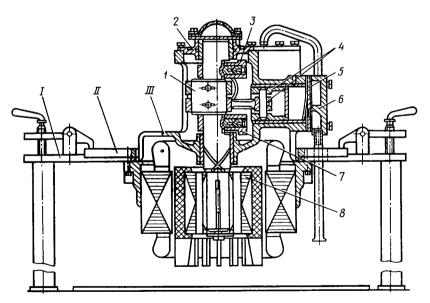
Приспособление для разборки и сборки герметичных компрессоров:
